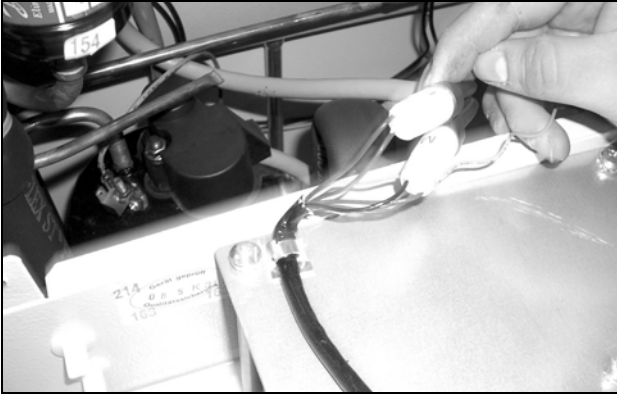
Demontáž ventilátoru vnějšího okruhu
